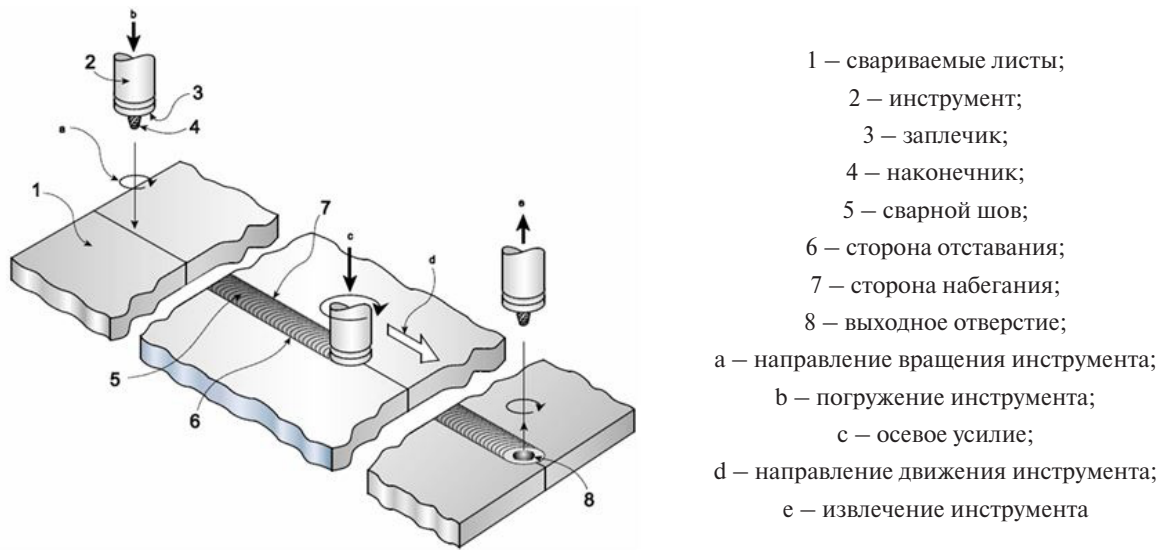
Общая схема сварки трением с перемешиванием [14]
